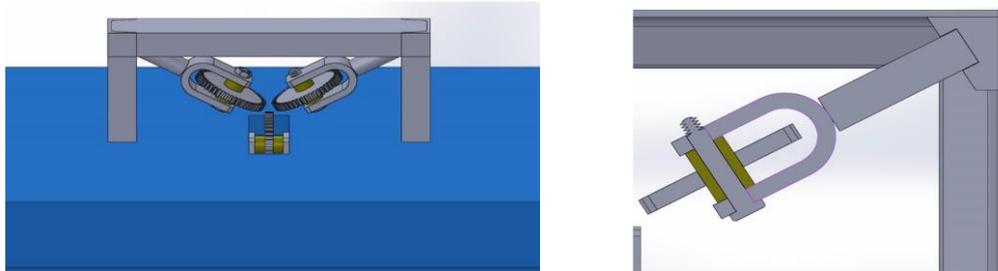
Arco soldado y corte ensamble vástago.
